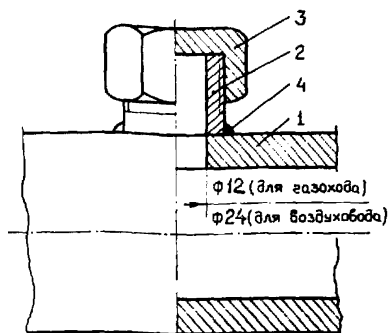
Схема оборудования точки замера: 1 - газоход; 2 - патрубок с резьбой на наружной стенке; 3 - накидная гайка (заглушка); 4 - место сварки патрубка со стенкой газохода (воздухохода)
